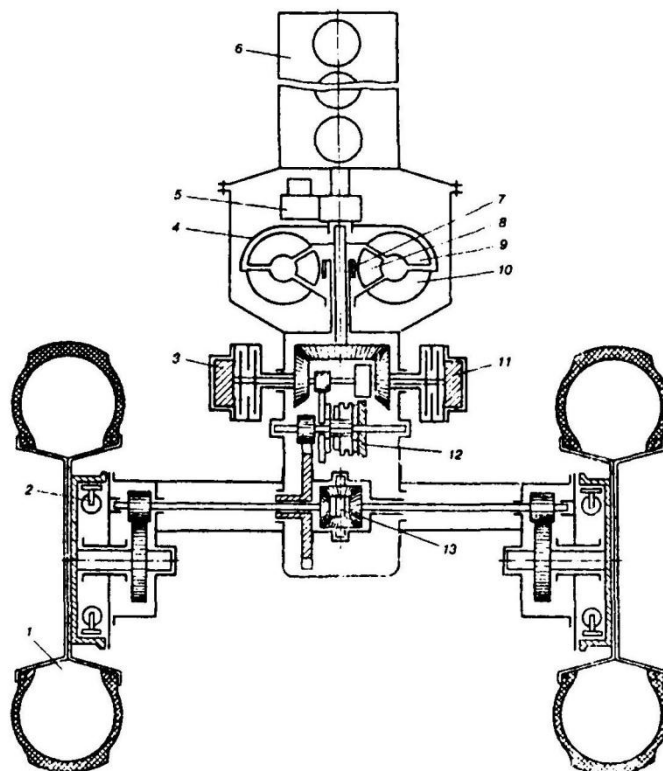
Гидродинамическая передача погрузчика с колесными редукторами
